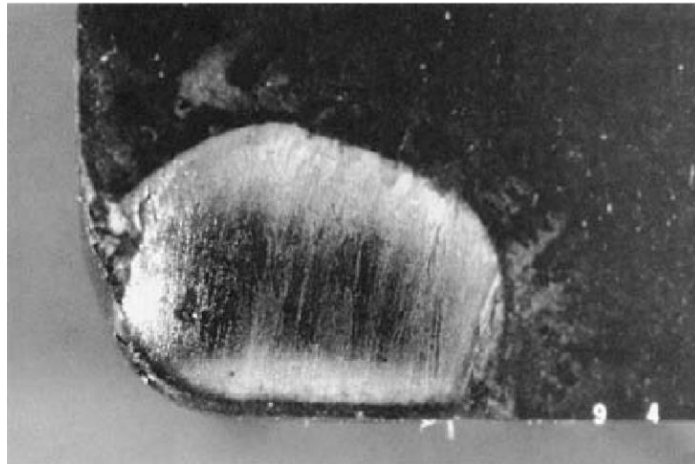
Esquema de la cara de ataque y del flanco de una herramienta de corte [2].
